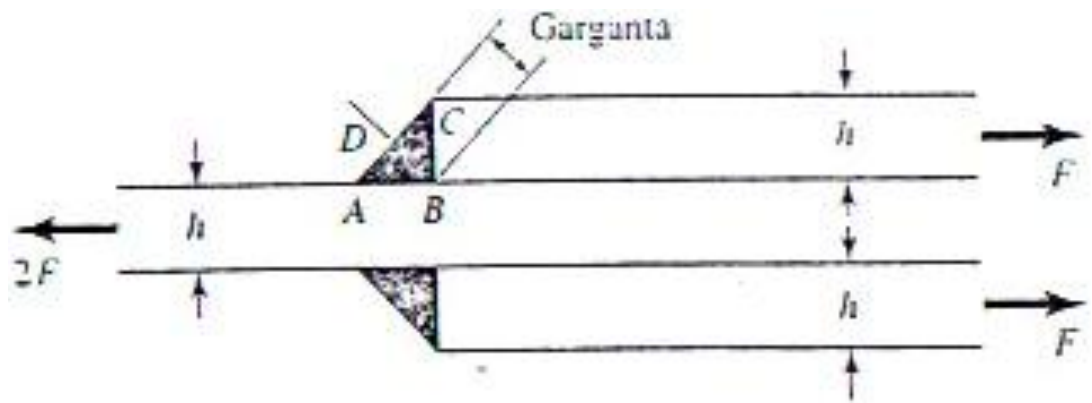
SOLDADURA DE FILETE (Ref. 7)
